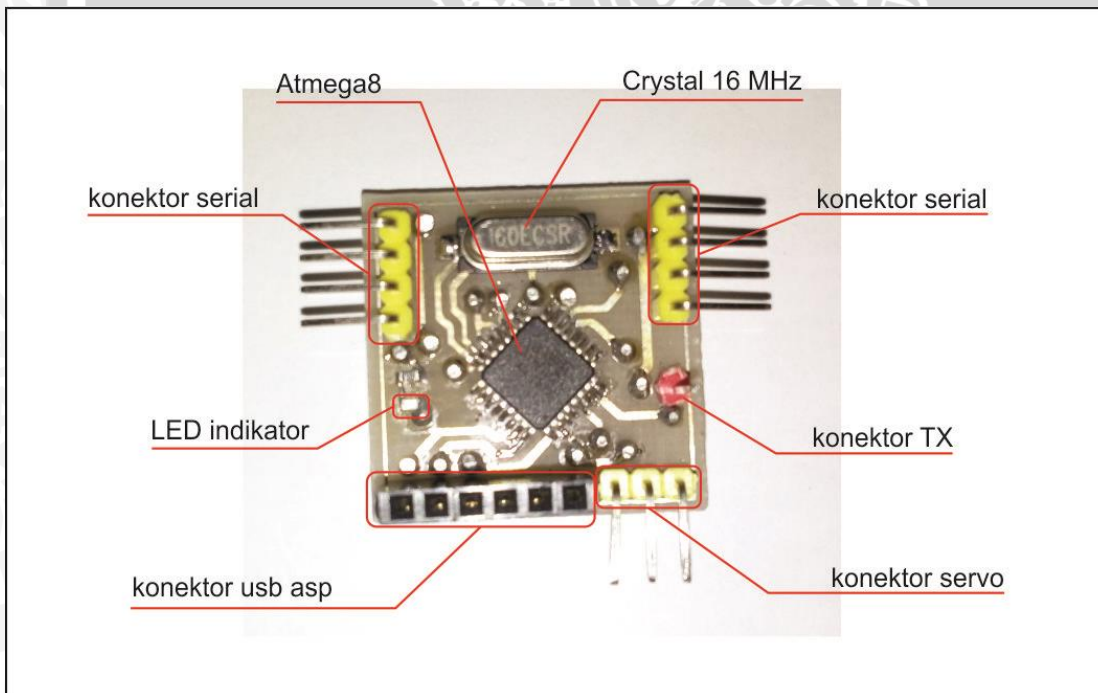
Layout PCB Top Layer Rangkaian Serial Driver
